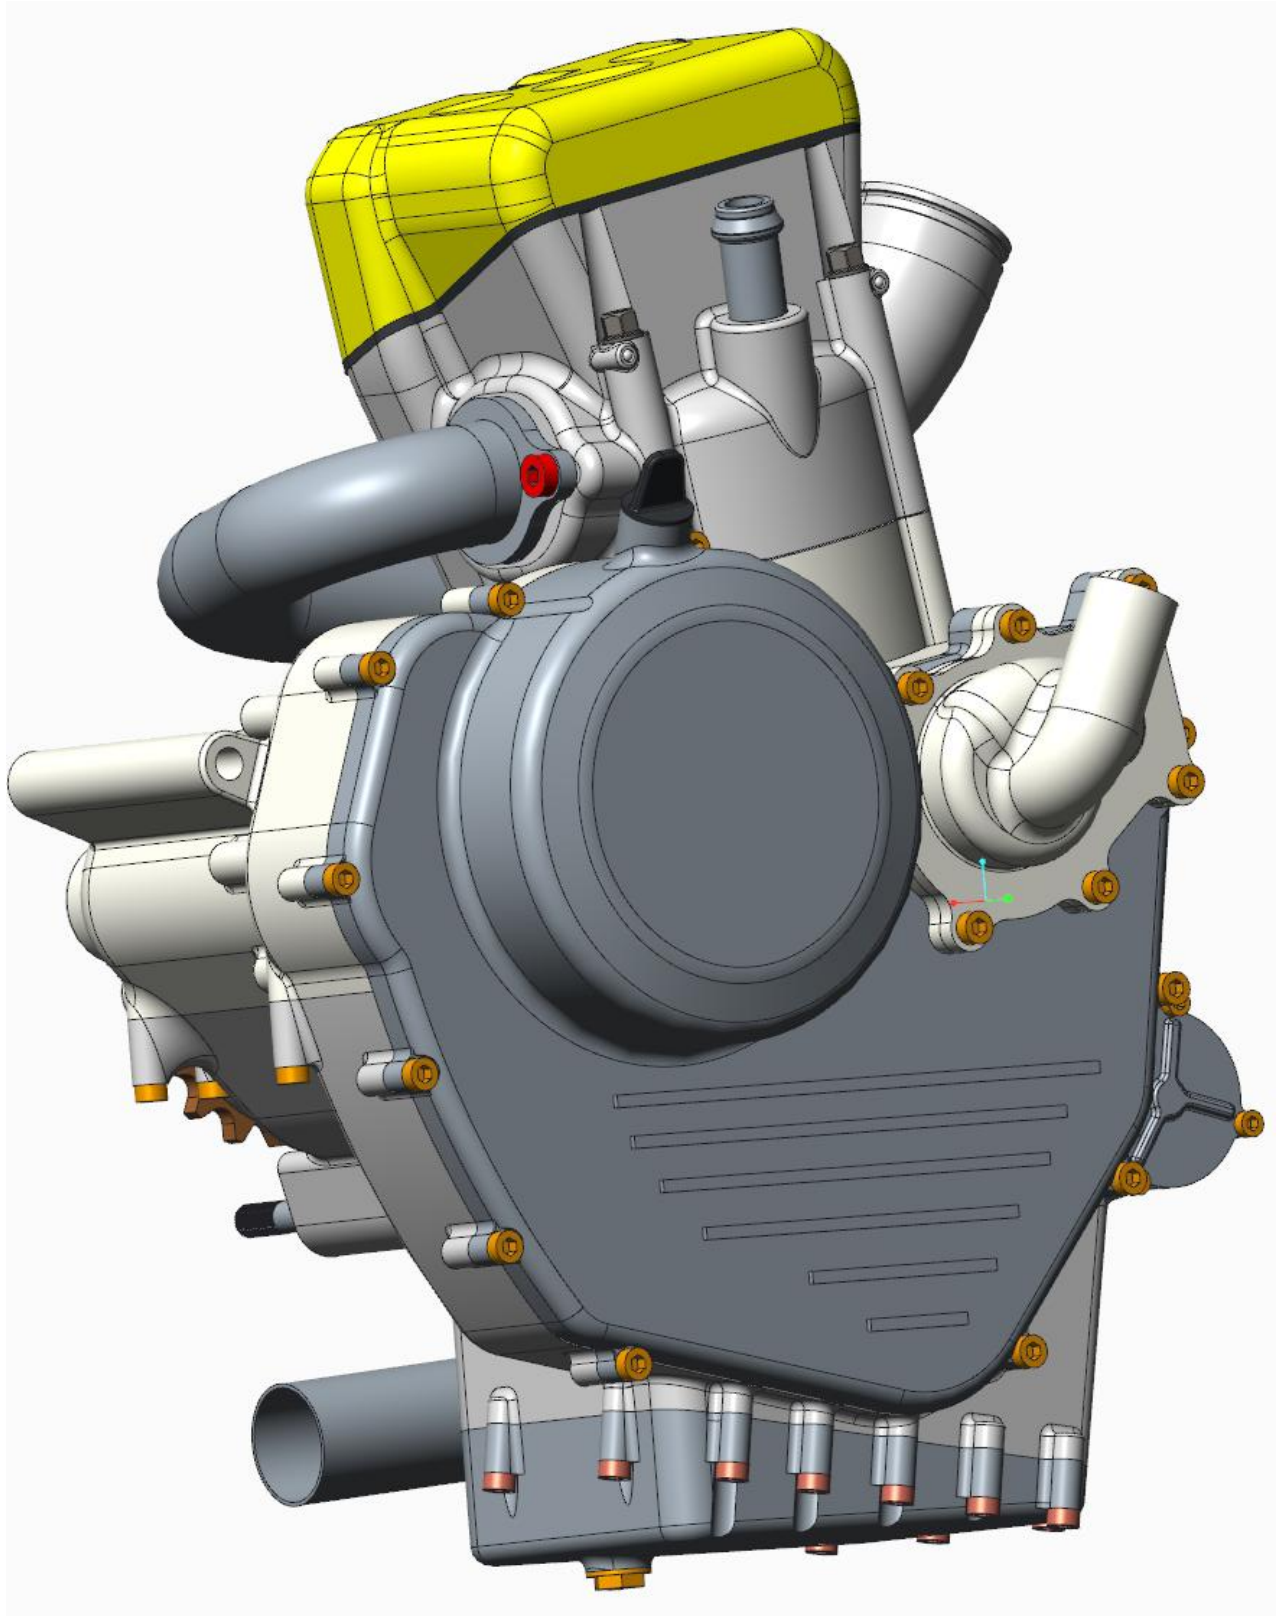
Kompletní model motoru, pohled Pravý-Přední
